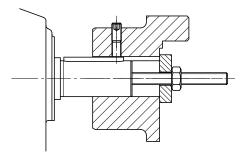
Beispiel einer einfachen Aufziehvorrichtung
